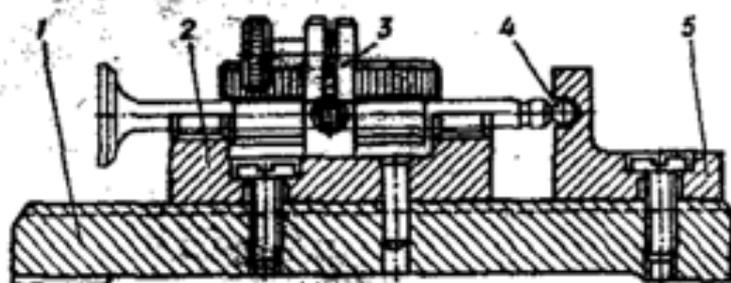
Проверка клапана на concentricity рабочей фаски головки и стержня: 1 - плита; 2 - призма; 3 - держатели; 4 - шарик; 5 - стойка; 6, 7 - индикаторы
